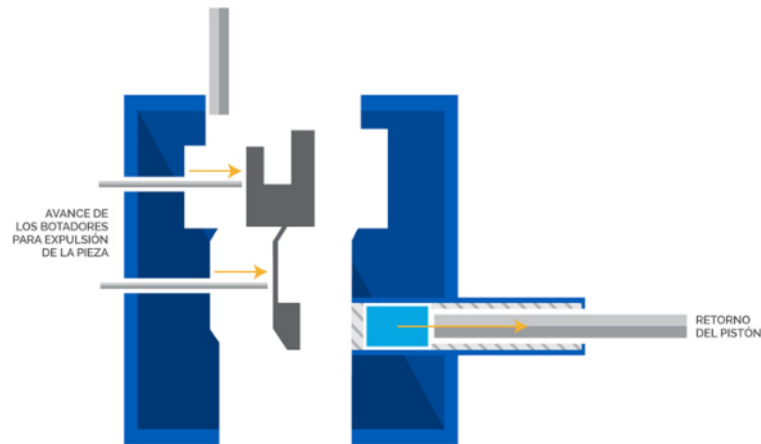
Los botadores empujan la pieza fundida fuera de la mitad del molde y el pistón regresa a su posición original.
